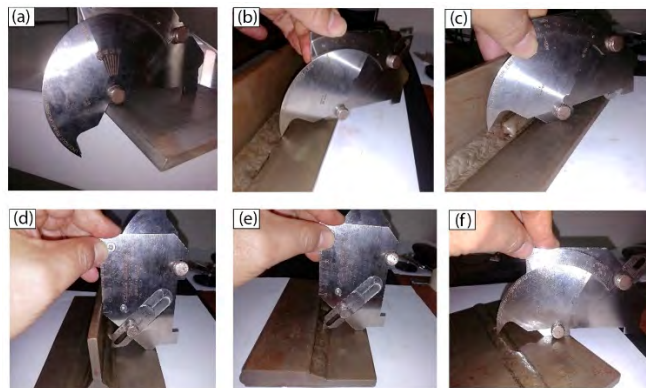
Disposición de Cambridge Gauge para verificar el tamaño de (a) ángulo de bisel, (b) socavado, (c) pierna en junta en T, (d) garganta en junta en T, (e) garganta en junta de solape, y (f) refuerzo en junta a tope
